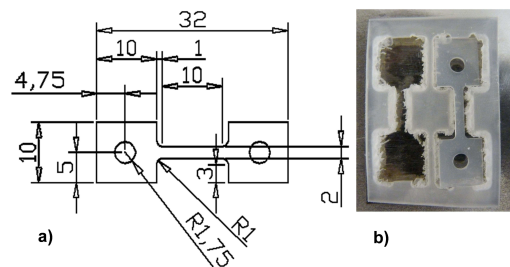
(a) Géométrie de la micro-éprouvette de déformation, d'épaisseur 1mm (Dimensions en mm) ; (b) micro-éprouvettes de LLDPE brutes après usinage.
